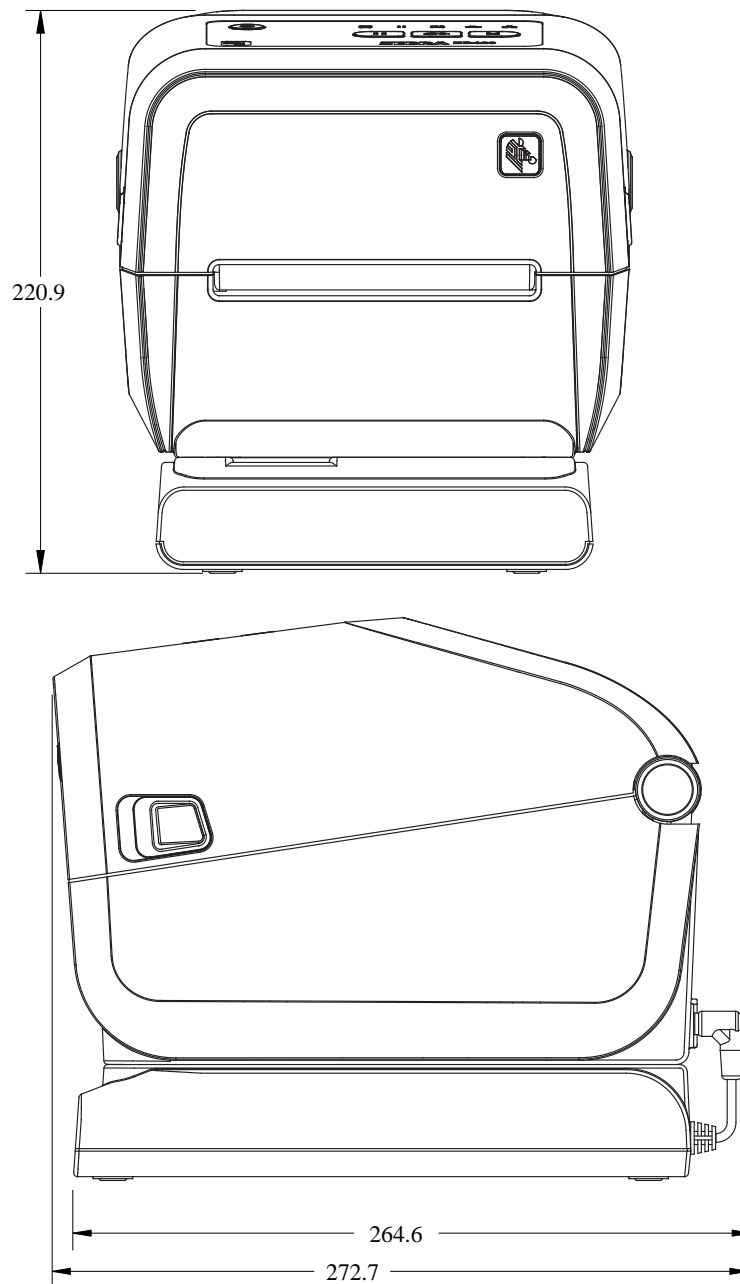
Modelos de impressora ZD421C (Transferência térmica do cartucho de fita) – dimensões da impressora com a opção Cutter (Cortador) instalada
